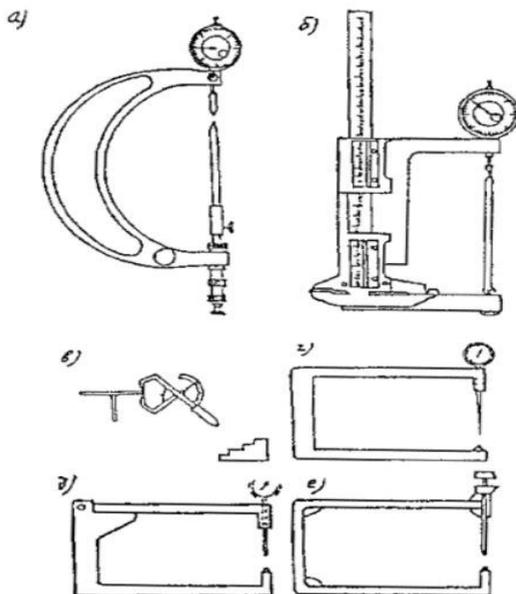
Приборы для измерения толщины стальных элементов конструкций. а) Микрометр; б) Штангенциркуль со стрелочным индикатором; в) Механический толщиномер; г) Коррозионно-метрическая скоба; д) скоба с раскрывающейся рамкой; е) раздвижная скоба. [6]
